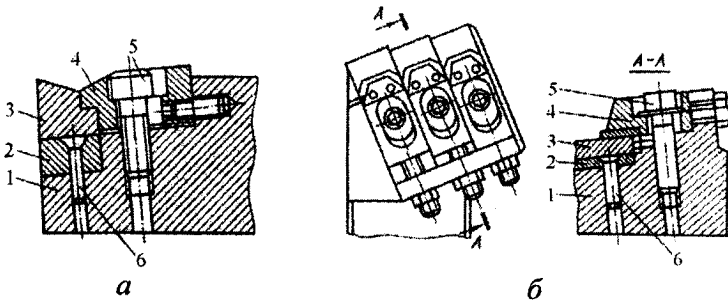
Токарні різці для важких умов роботи: *а* – фіксування прихвата по опорних поверхнях державки; *б* – конструкція, що розподіляє припуск між трьома пластинами: 1 – корпус; 2 – підкладка; 3 – пластина; 4 – прихват; 5 – гвинт
